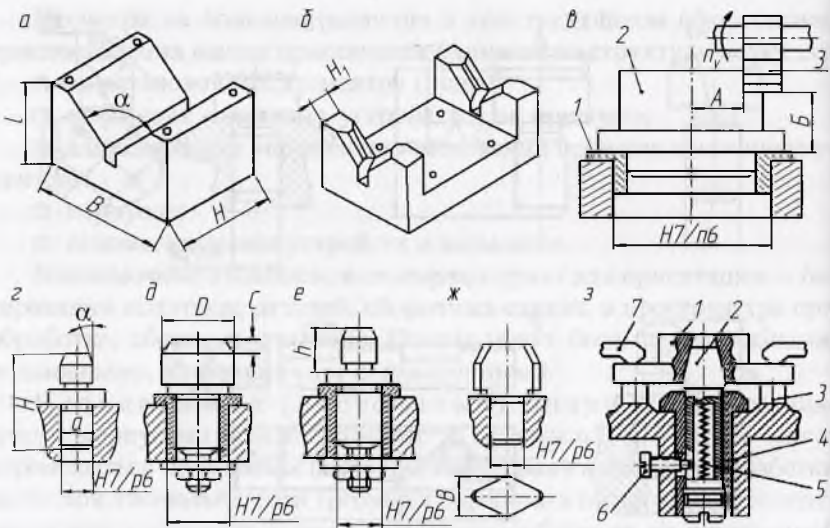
Элементы для базирования заготовок по наружным (а–в: 1 — установочная втулка; 2 — заготовка; 3 — инструмент в виде фрезы); внутренним цилиндрическим (г–ж) и коническим (з) поверхностям: а, б — призмы широкая и узкая двоянная; г–е — пальцы цилиндрические постоянные и сменные, с буртом и без бурта; ж — палец цилиндрический срезанный (ромбический) без бурта; з — палец конический плавающий с опорными пластинами на его корпусе
